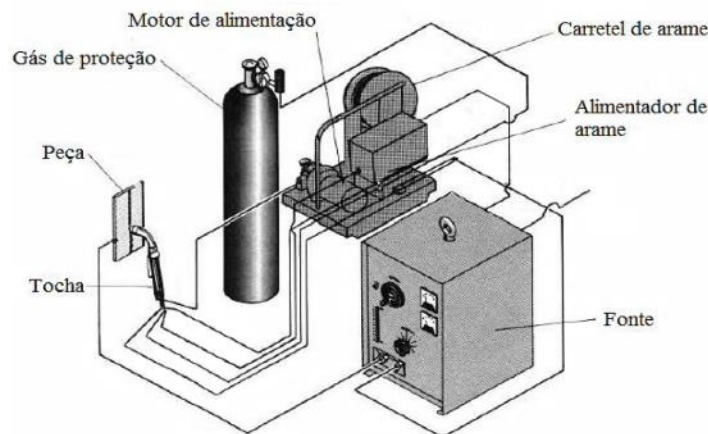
Esquema genérico do equipamento para soldadura GMAW [15]
